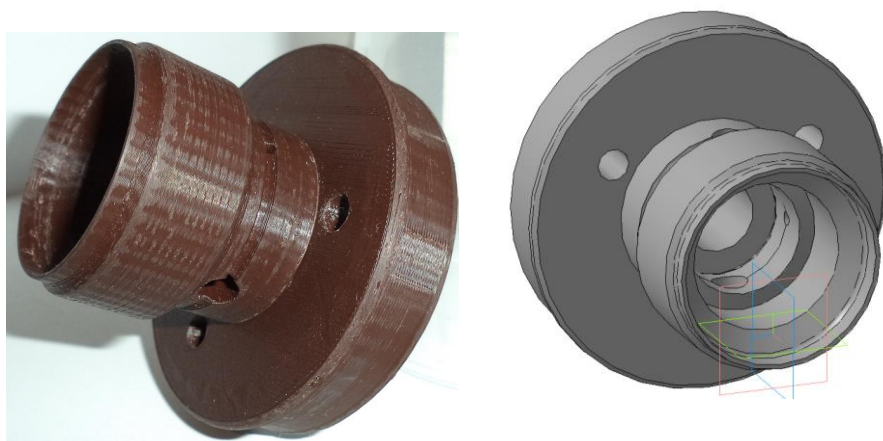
3D-модель детали и её прототип, распечатанный на 3D-принтере
